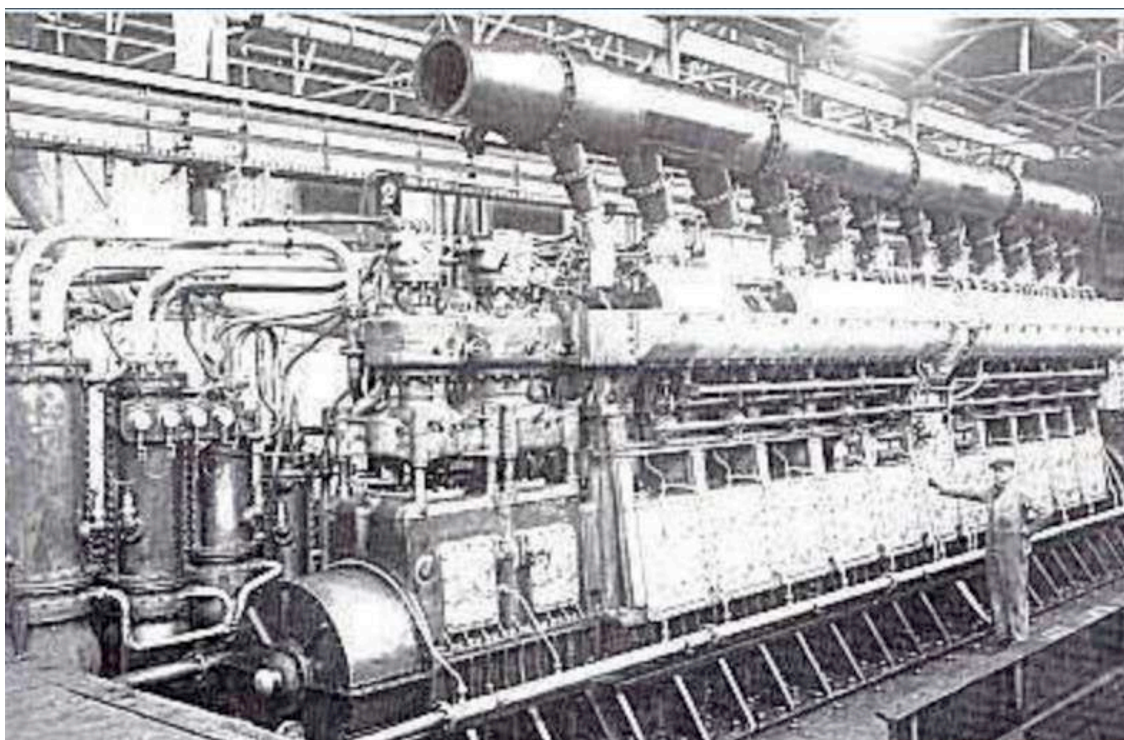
Motore sovralimentato di dr del Thames in montaggio in officina
